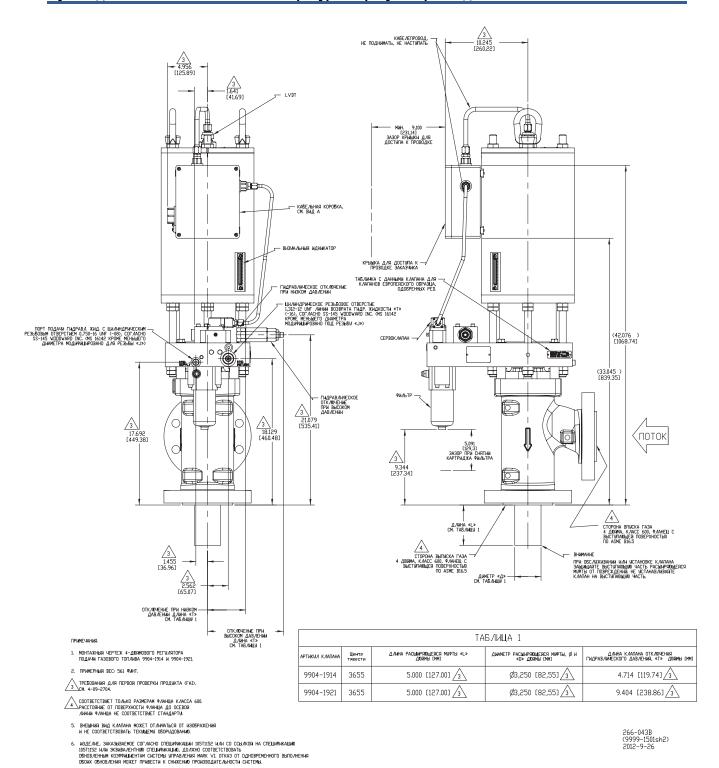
Габаритный чертеж регулятора SonicFlo (4 дюйма, класс 600)
